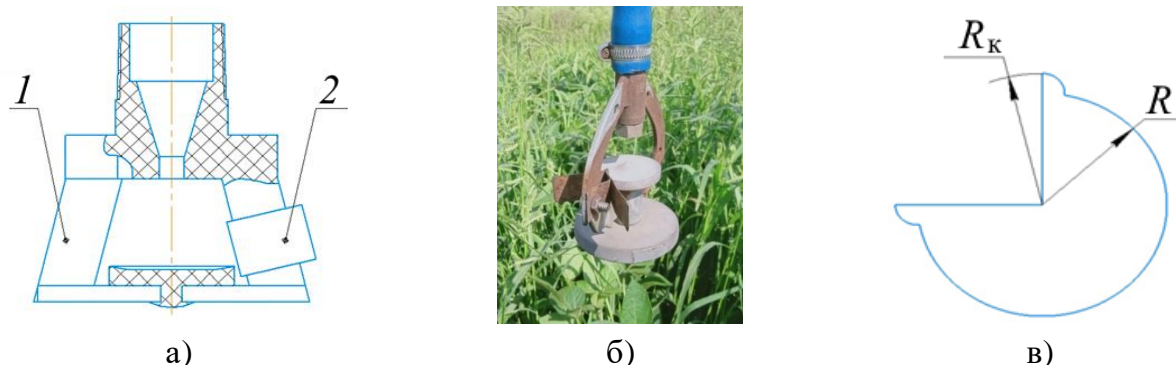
Схема конструкции и зона орошения дождевальной насадки секторного полива
